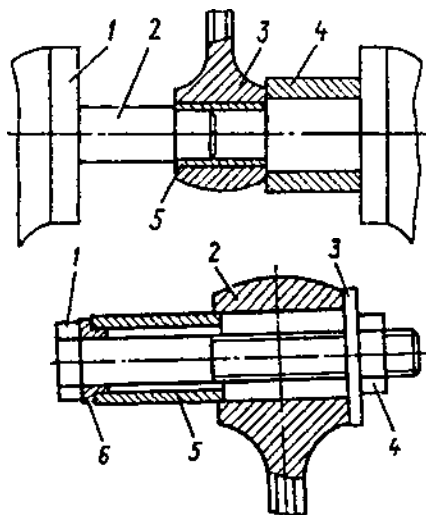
Запрессовка втулки верхней головки шатуна с помощью приспособления:
